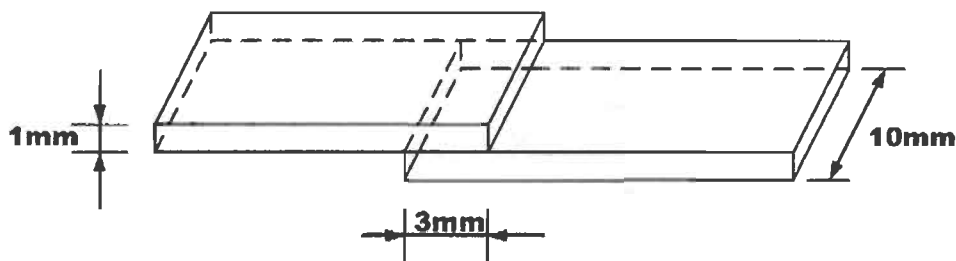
Especimen de uniones por brazing de Aluminio 3003.
